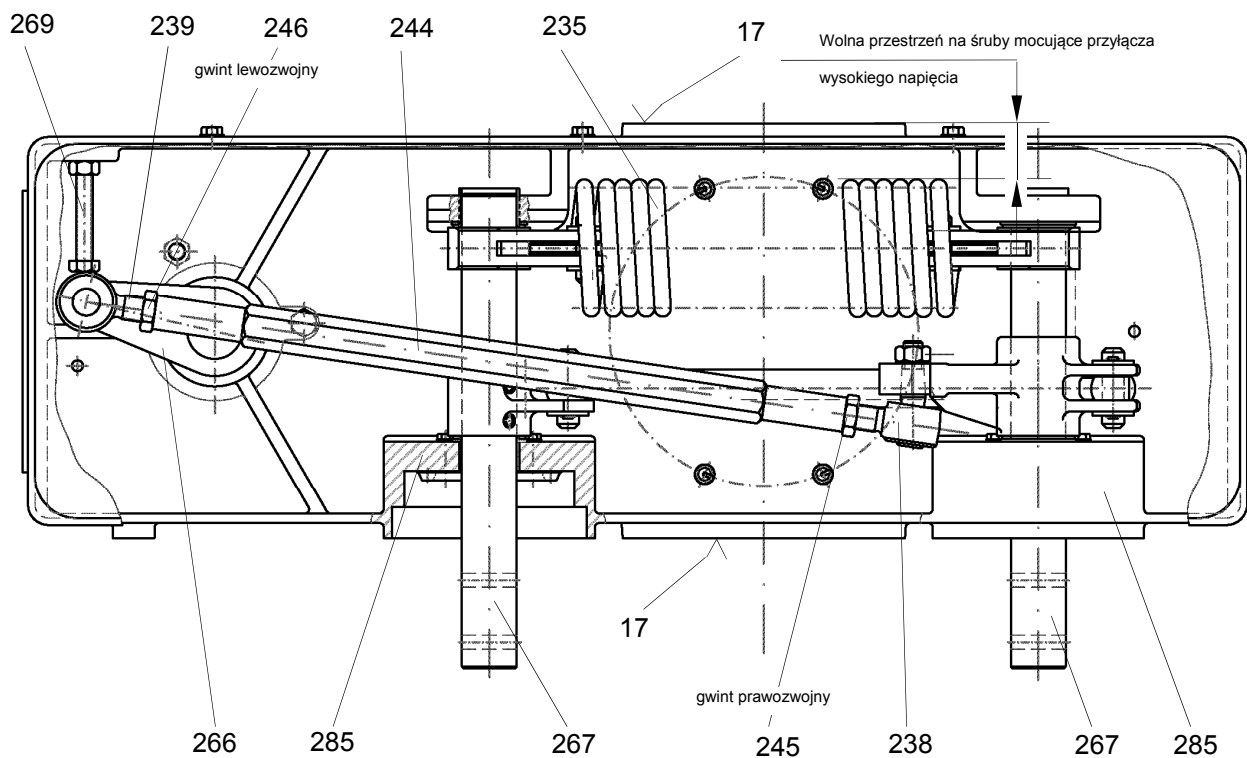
Instalacja skrzyni przekładni, górnego elementu pośredniego i izolatorów. Połączenie kołnierza łączącego 230 i izolatora obrotowego
